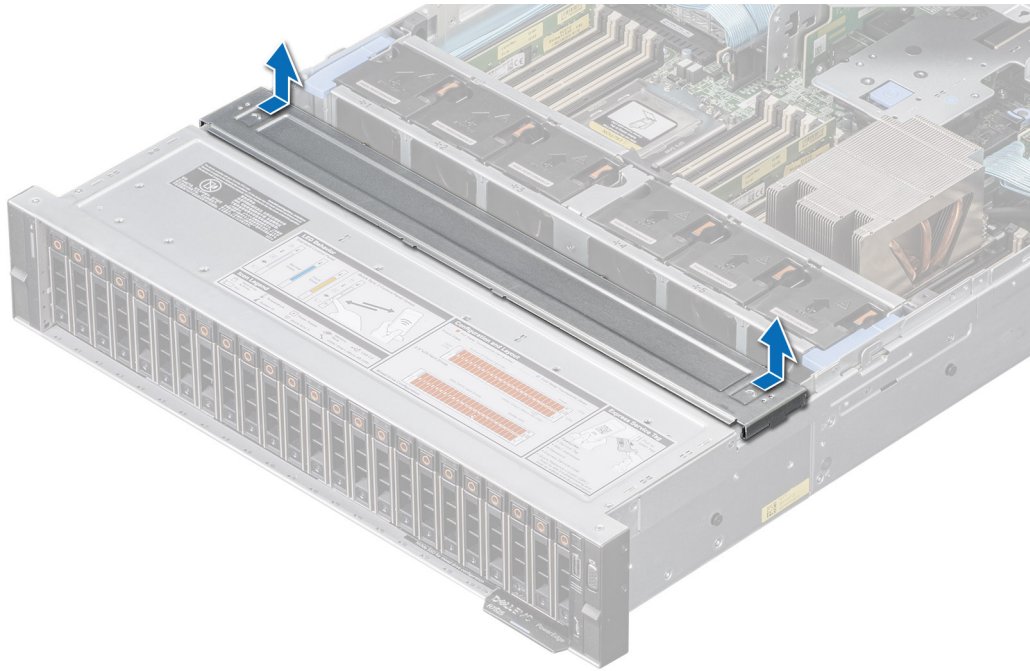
Laufwerkrückwandplattenabdeckung entfernen
